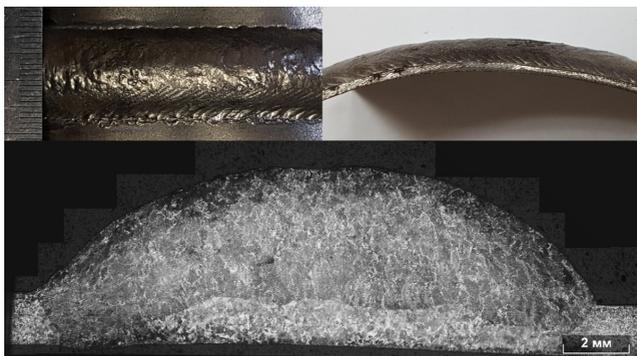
Наплавка валика, выполненная с поперечными колебаниями горелки
